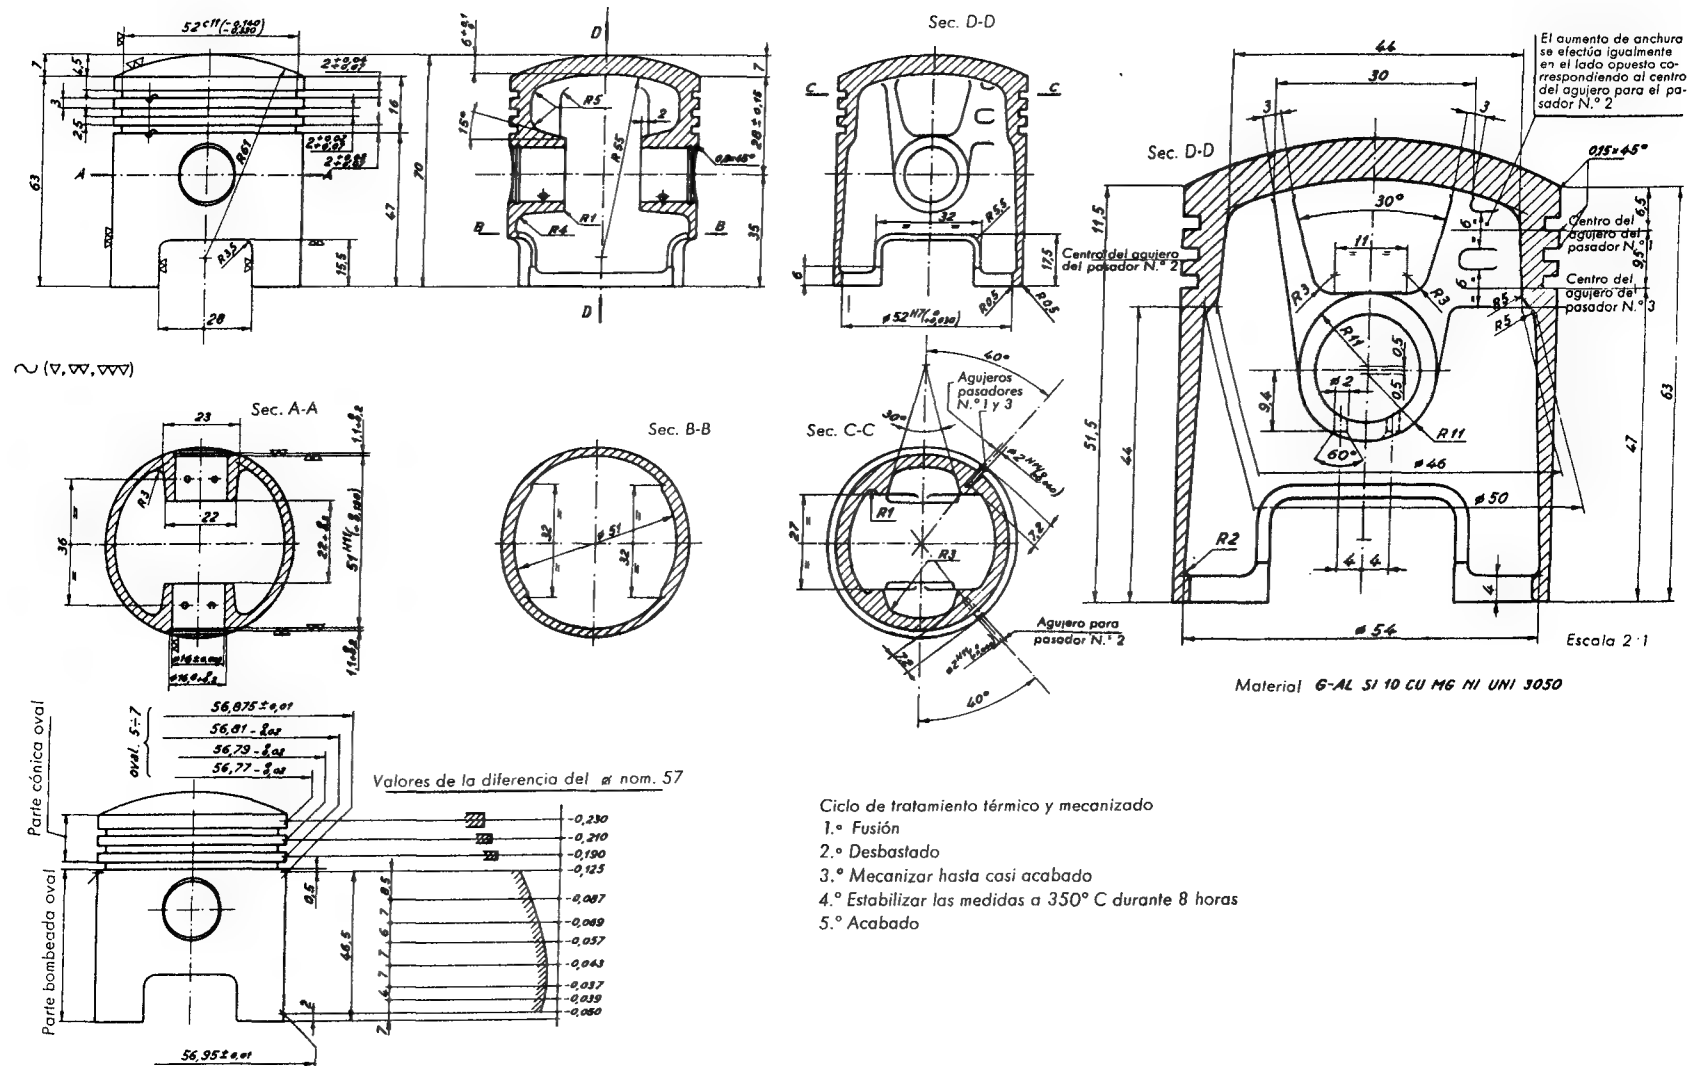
, 527. Pistón para motor de Lambretta (Innocenti).
